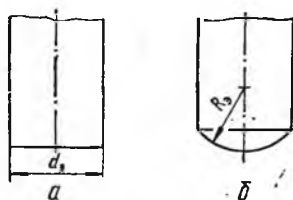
Плоский (а) и сферический (б) профили контактной поверхности электродов для точечной контактной сварки металлических листов.
